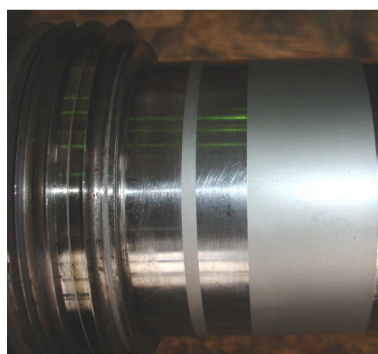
Следы электроэрозии на шейке ротора КВД в месте установки опорного подшипника и его уплотнения
